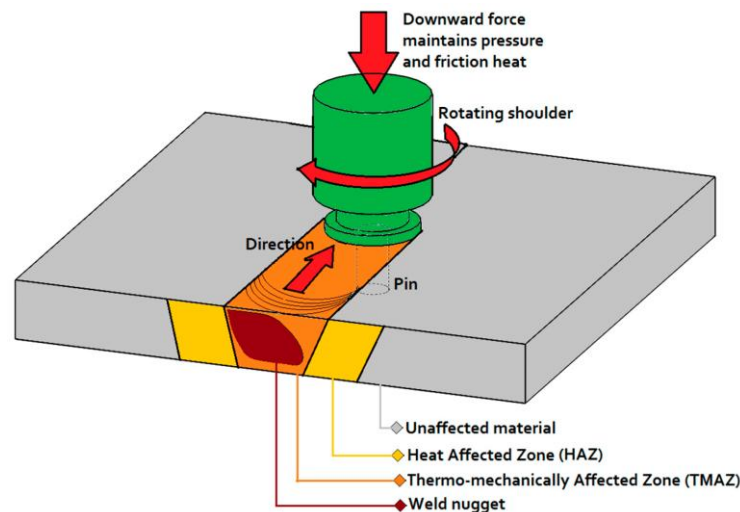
Esquema del proceso de soldadura "Friction Stir Welding" (Aheri, H., Kilpatrick, M., Norvalls, M., Harper, W. J., Koester, L. W., Bigelow, T., & Bond, L. J. (2019). Investigation of nondestructive testing methods for friction stir welding)
